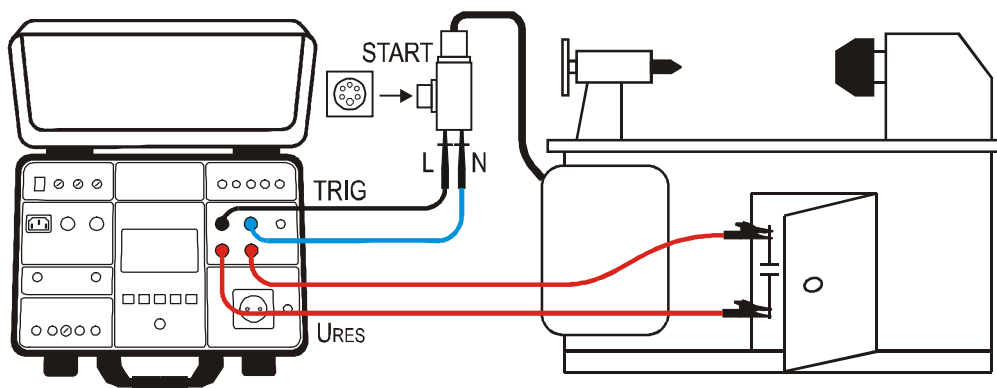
Ligação das ponteiros de teste para medição URES INT em máquinas ligadas 1P/3P
